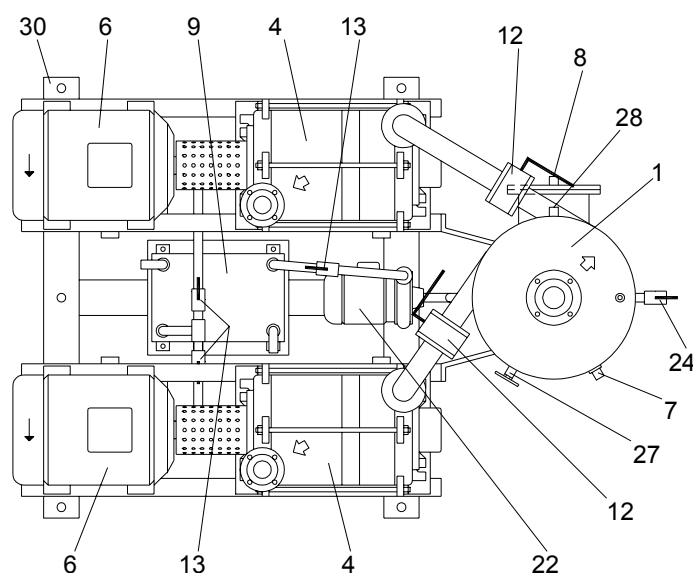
Двойная система полной рециркуляции (вид сверху)
